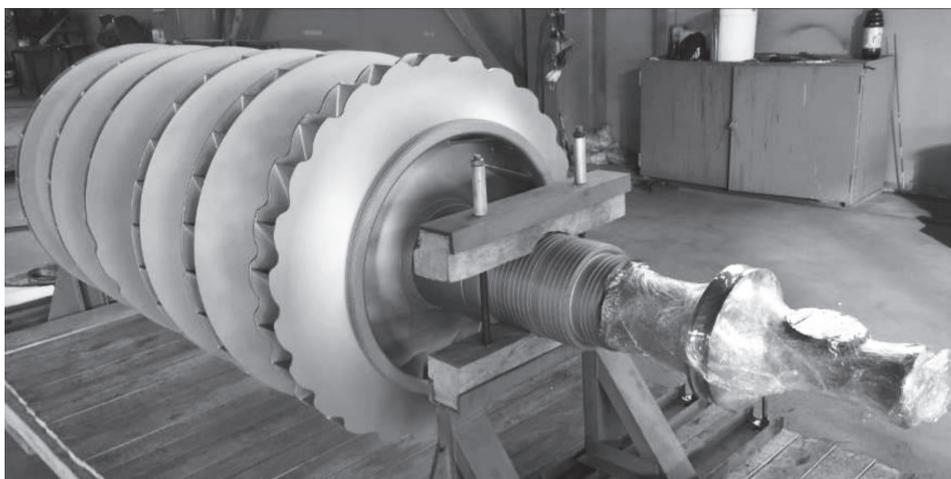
Модернизированный ротор ЦНД (компрессор типа 2MCL1006+2MCL456)
